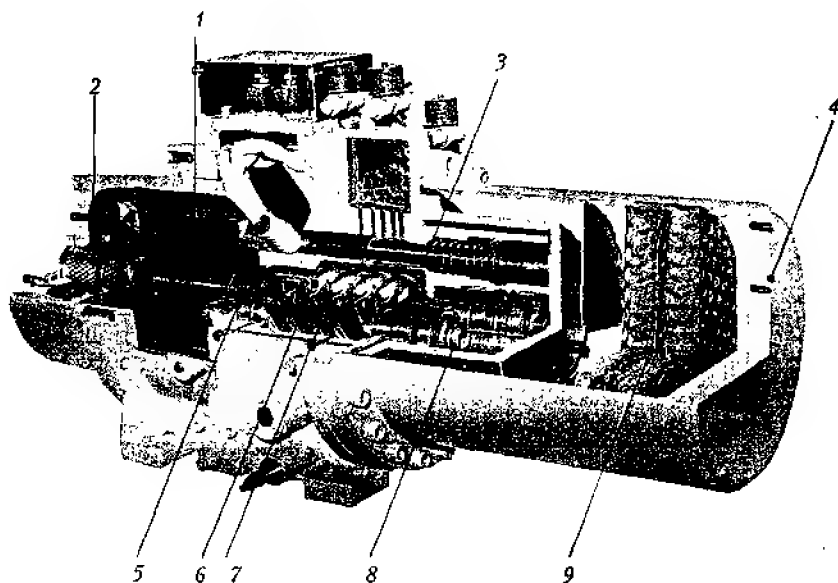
Общий вид двухвинтового компрессора (в разрезе):
